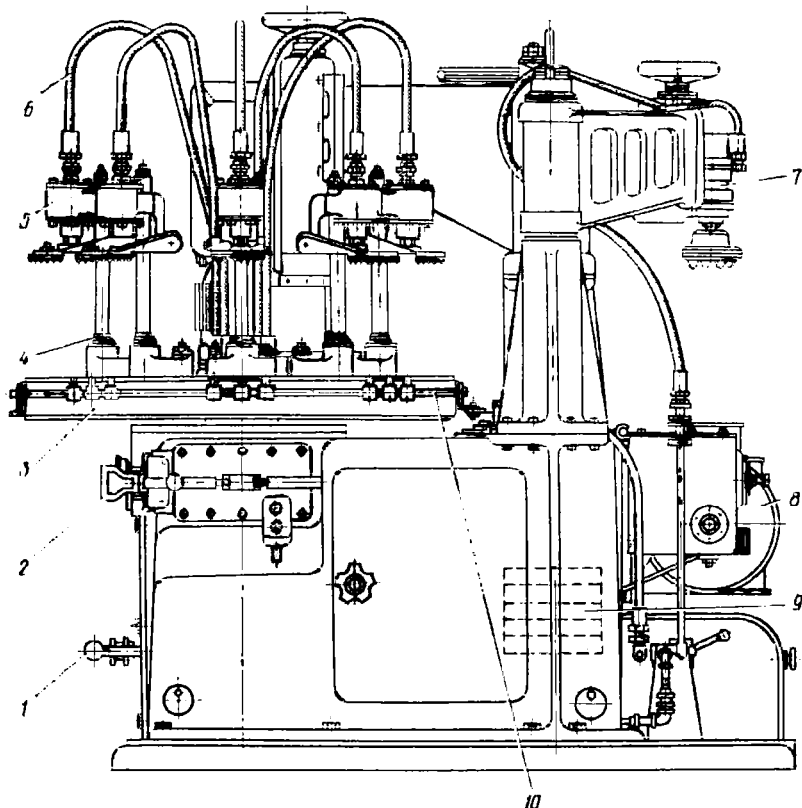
Схема карусельного фрезерно-шлифовального станка Ф1К-2А:
